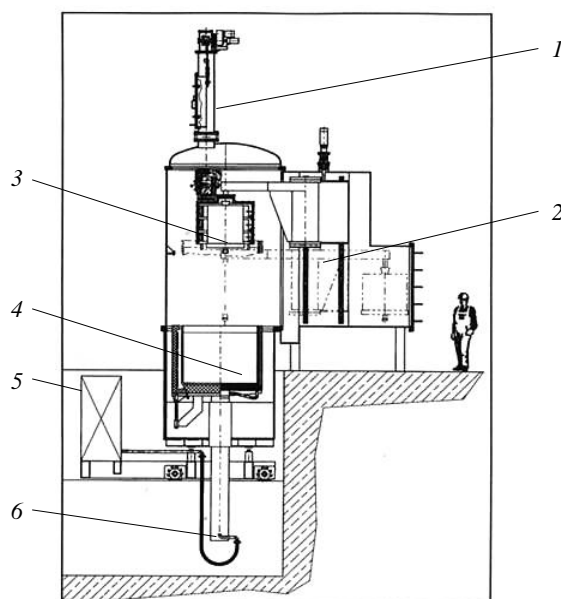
Установка VIM-IC 10 DS/SC/LMC для литья крупногабаритных лопаток из жаропрочного сплава: 1 – механизм для загрузки шихты и перемещения подвески с формой; 2 – шлюзовая камера для выгрузки печи подогрева формы; 3 – трехзонная печь подогрева формы; 4 – ванна с жидкометаллическим охладителем; 5 – шлюзовая камера для выгрузки ванны с жидкометаллическим охладителем; 6 – механизм для подъема ванн с жидкометаллическим охладителем
